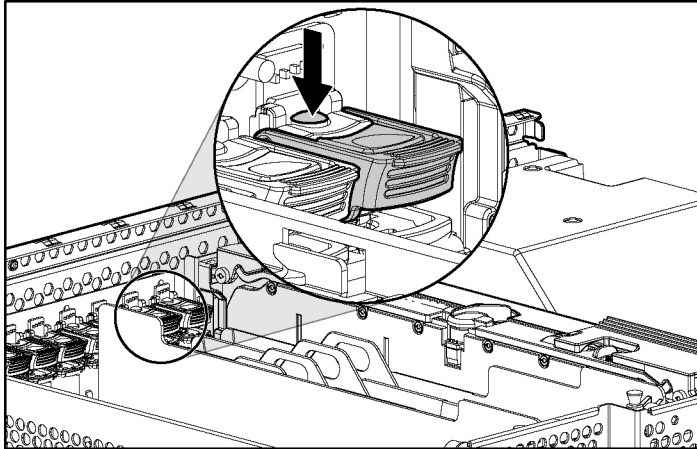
Ausschalten des Steckplatzes mit der dunkelroten PCI-Hot-Plug-Taste
